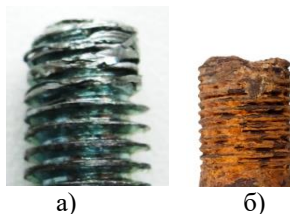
Поверхность метрической резьбы: а – смятие резьбовой поверхности; б – коррозия резьбовой поверхности.
